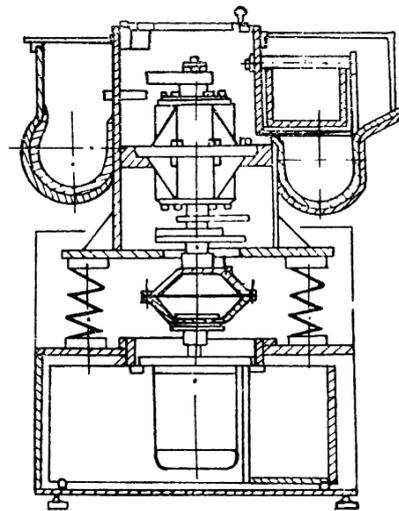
Схема галтовочного станка с торообразной рабочей камерой [5]
